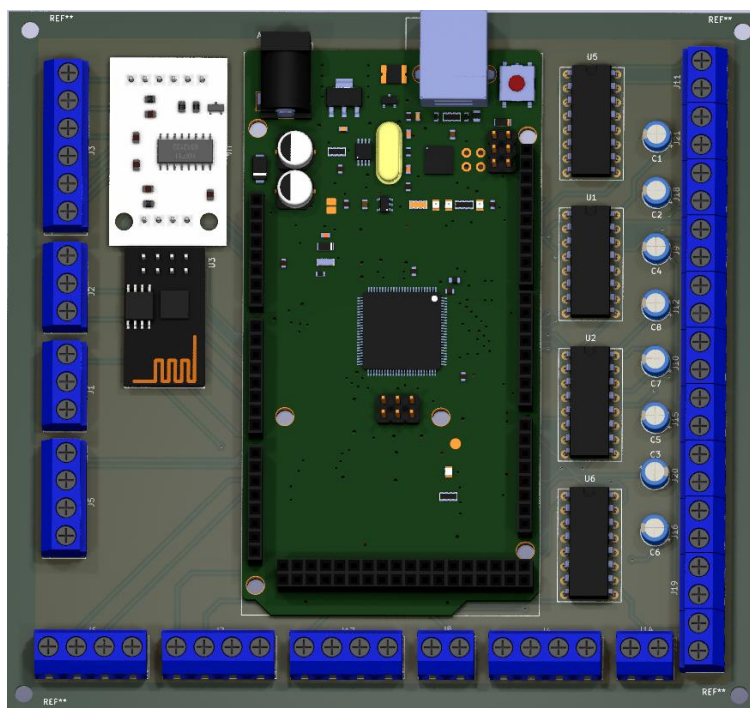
PCB diseñada con los componentes soldados
